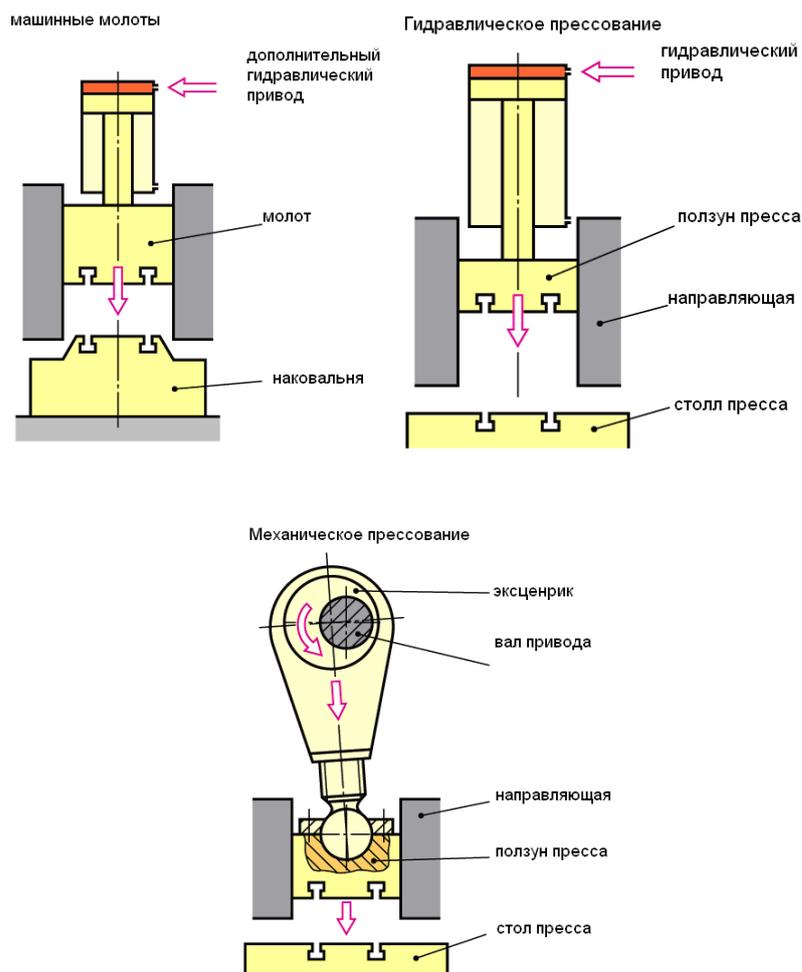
Схемы исполнительных механизмов оборудования для механизированнойковки
